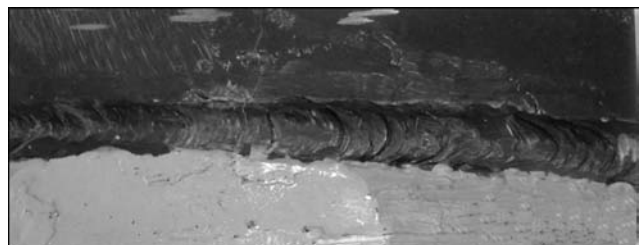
Характерный образец с катаной поверхностью, сварным швом и окрашенной поверхностью, содержащий эксплуатационную трещину, обнаруживаемую дефектоскопами типа «Малыш-М»
